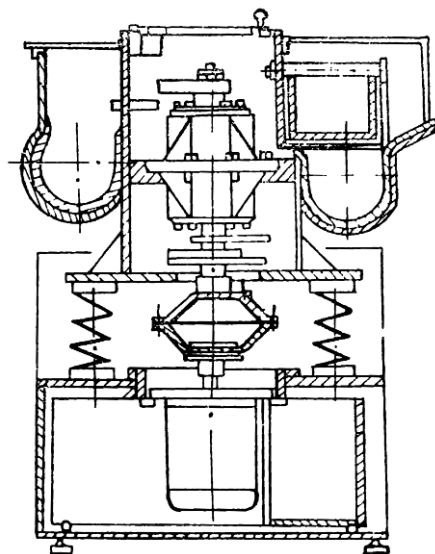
Схема галтувального станка с тороподібною робочою камерою
